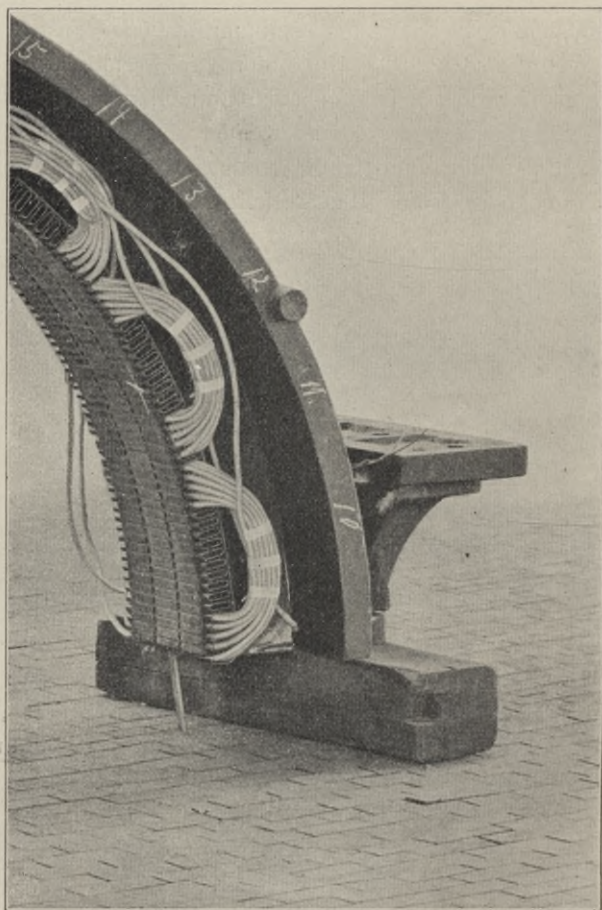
Ein Theil des Ankers des Schuckert'schen Drehstromerzeugers mit Wicklung.
